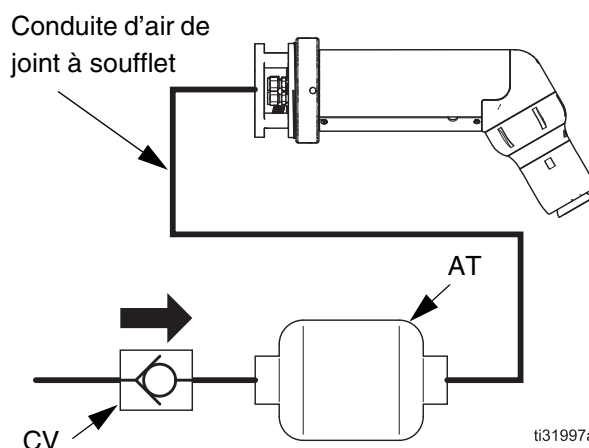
Conduite d'air du joint à soufflet avec réservoir d'accumulation et clapet anti-retour
